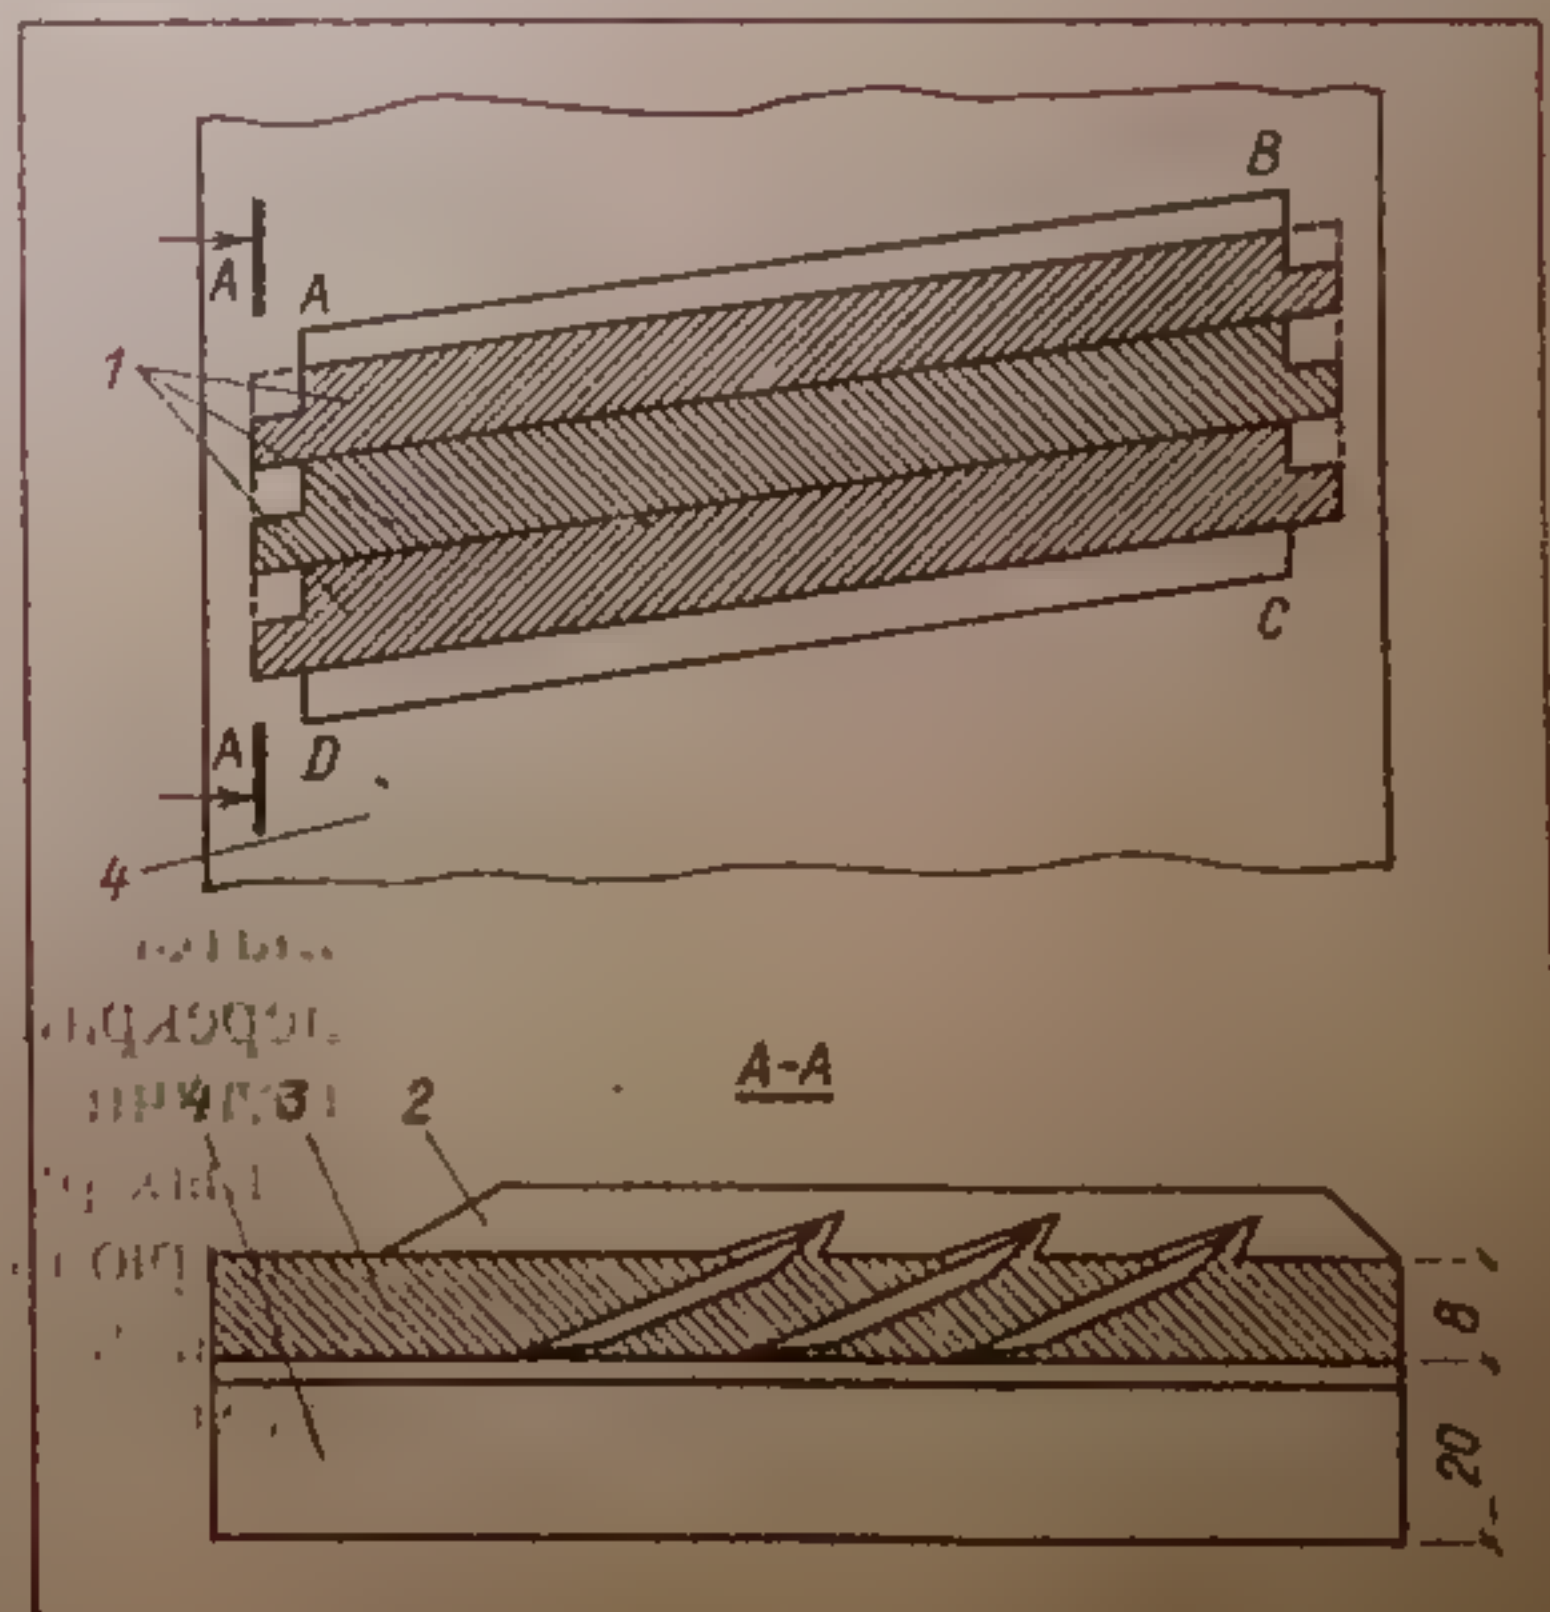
Схема установки ножей на столе шинковки: 1 — ножи; 2 — накладная планка; 3 — стол; 4 — уголок; ABCD — отверстие для ножей
